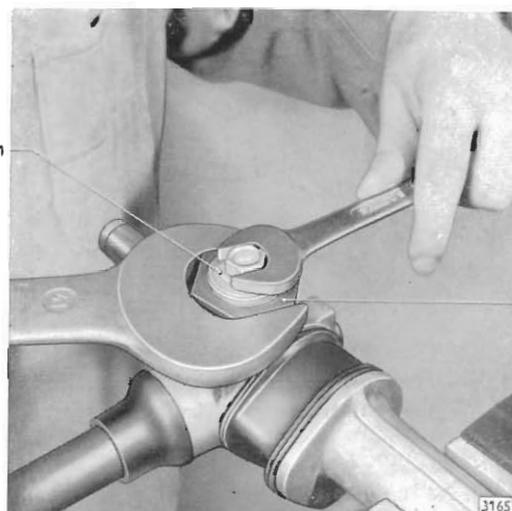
Sechskant-Gegenmutter für Einstellschraube lösen (am ausgebauten Lenkgetriebe – ohne Spurstangen – gezeigt)
